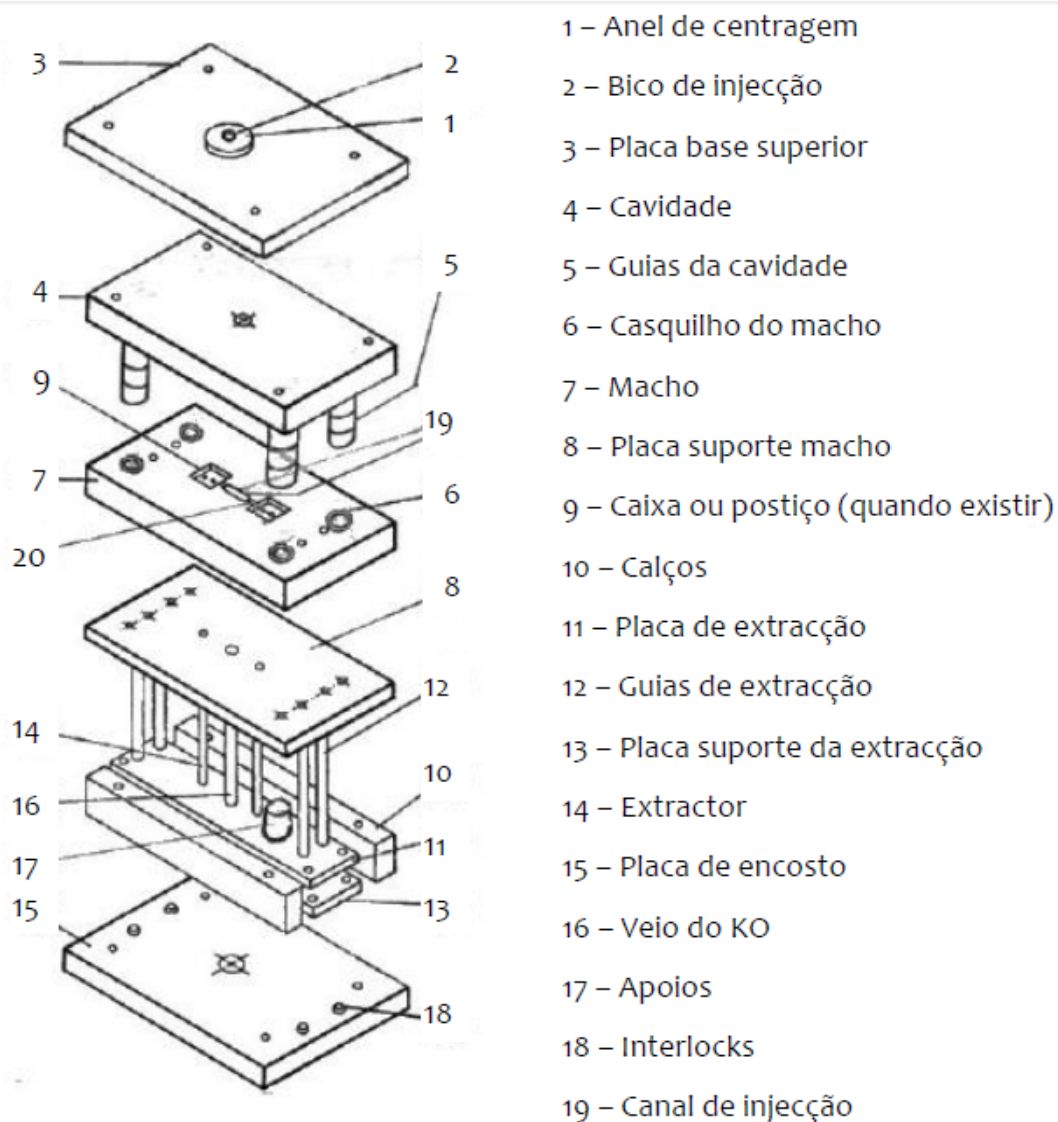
Desenho esquemático de um molde de duas placas, vista explodida [Reinert, 2004].
